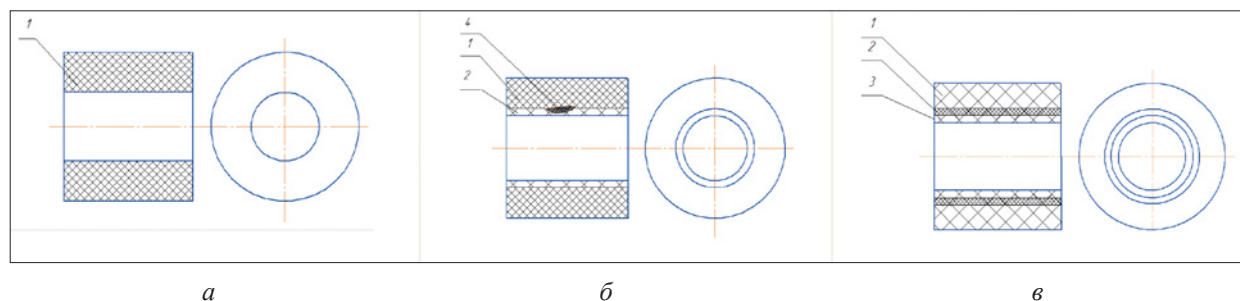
Схема конструкции стенки трубы системы вентиляции из ПКМ:
